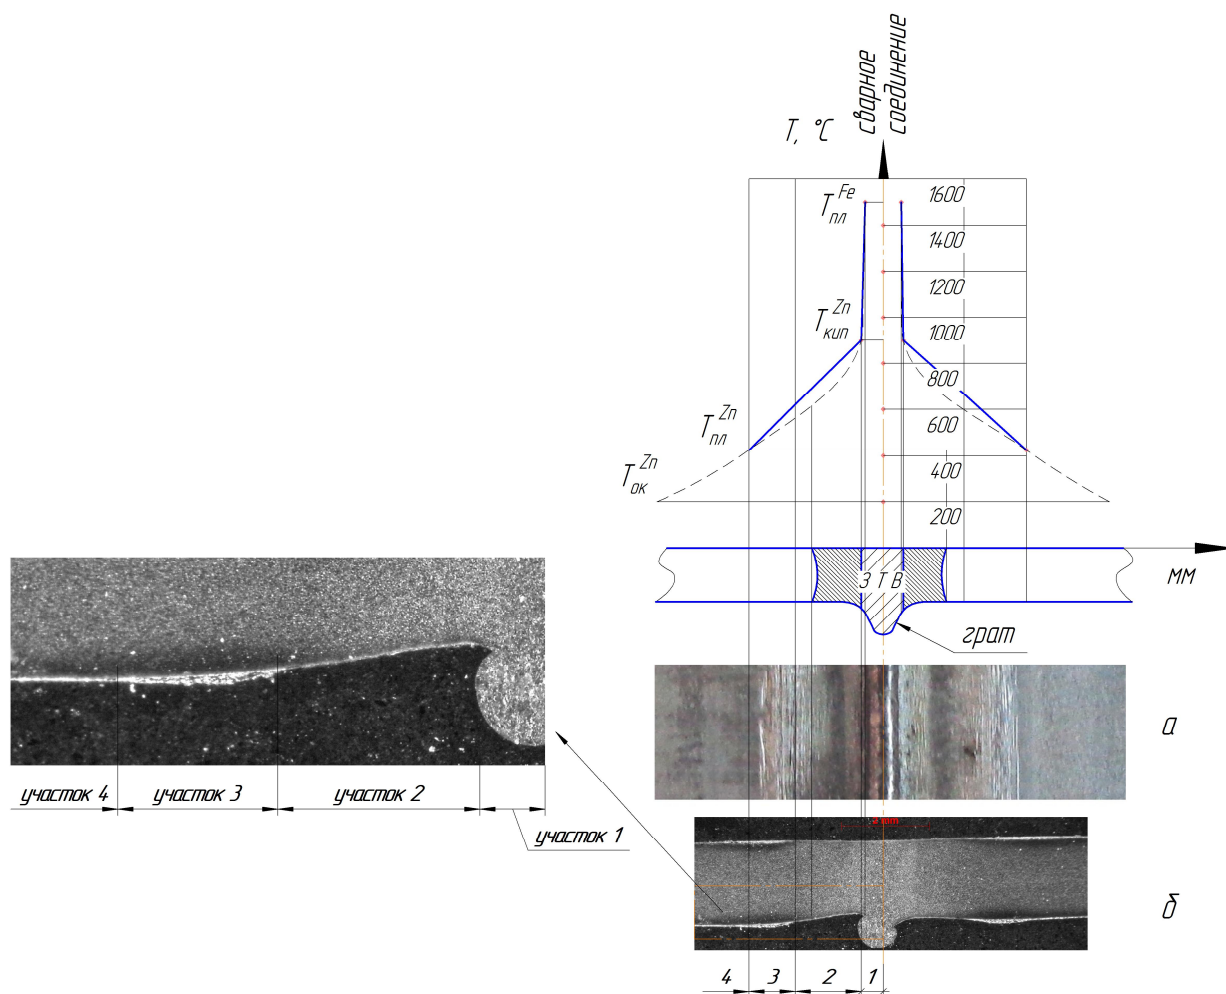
Область повреждения цинкового покрытия при сварке ТВЧ и график распределения температуры по ширине сварного соединения: а – вид внутренней поверхности зоны сварного соединения (образец №6); б – вид поперечного шлифа зоны сварного соединения (образец № 6)
